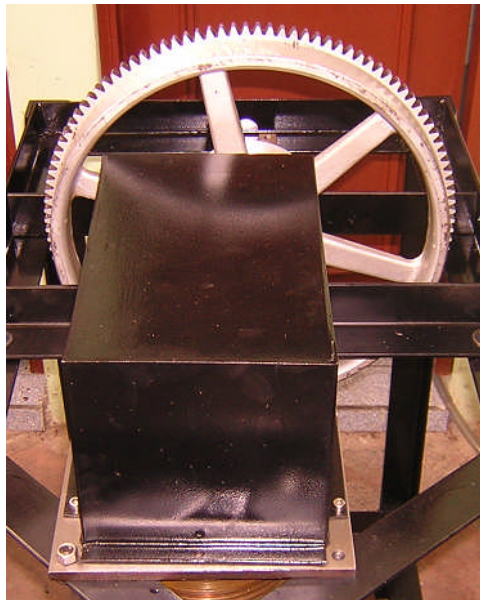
Fotografía del motor, usando un engranaje-polea como volante.
